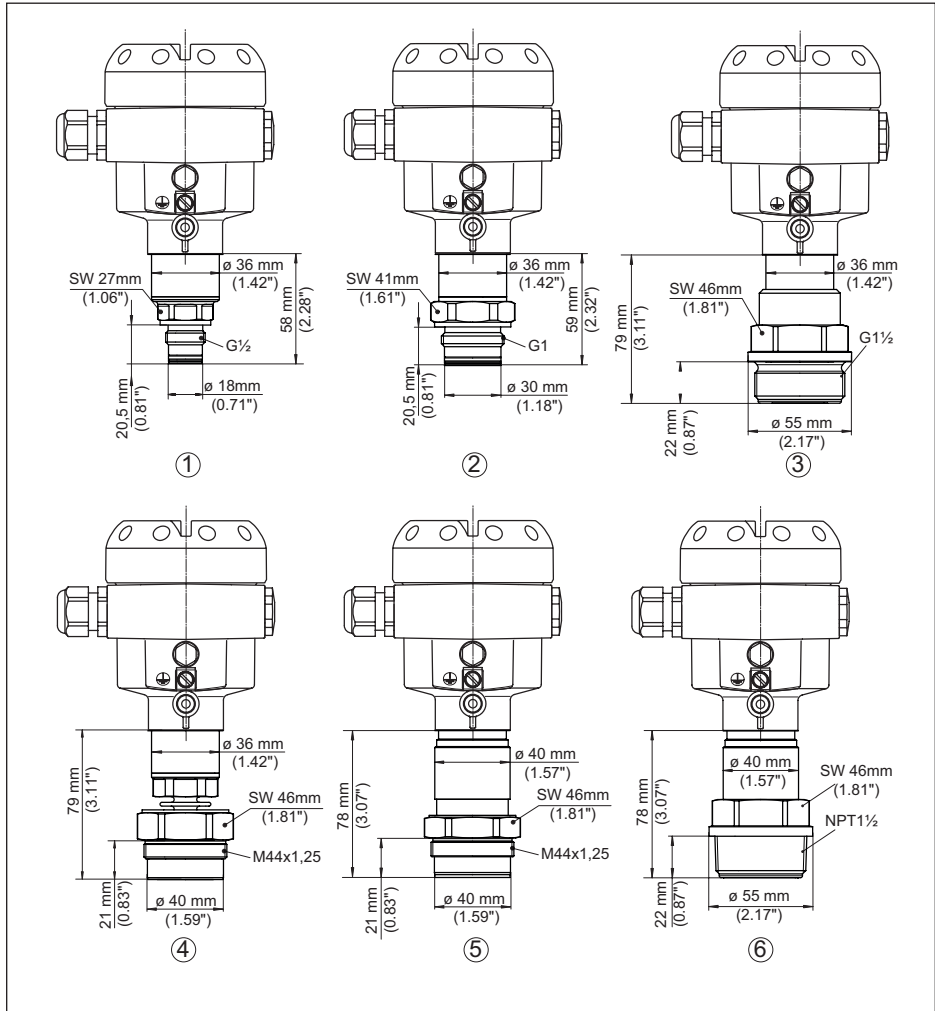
IPT-2x, Gewindeanschluss frontbündig
